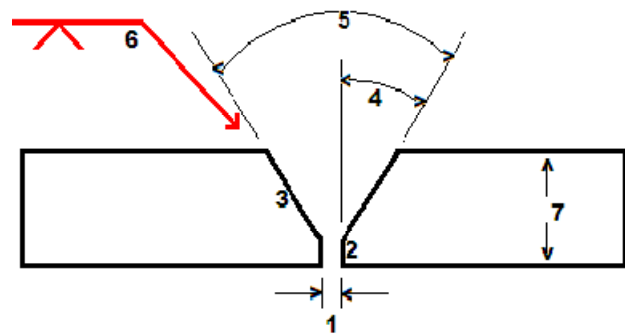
Partes de la junta sin soldar. Fuente Instituto chileno de soldadura. Página 23.
